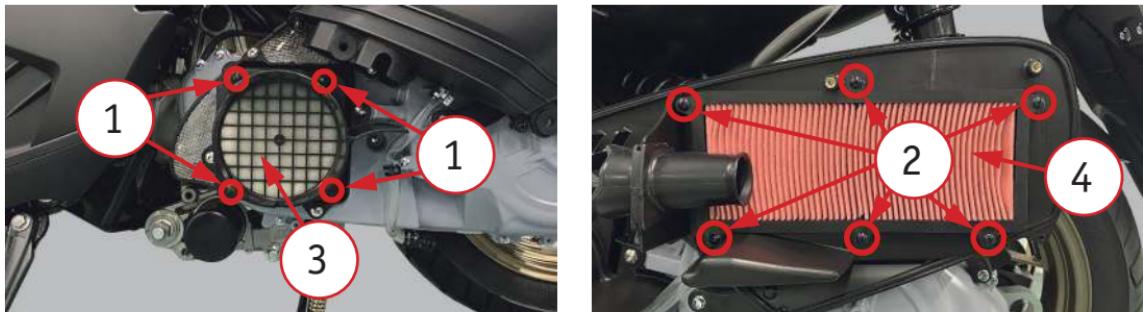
Замена воздушных фильтров: 1 – винты крепления воздушного фильтра вариатора; 2 – винты крепления воздушного фильтра двигателя. 3 - воздушный фильтр вариатора (поролон); 4 - воздушный фильтр двигателя.
